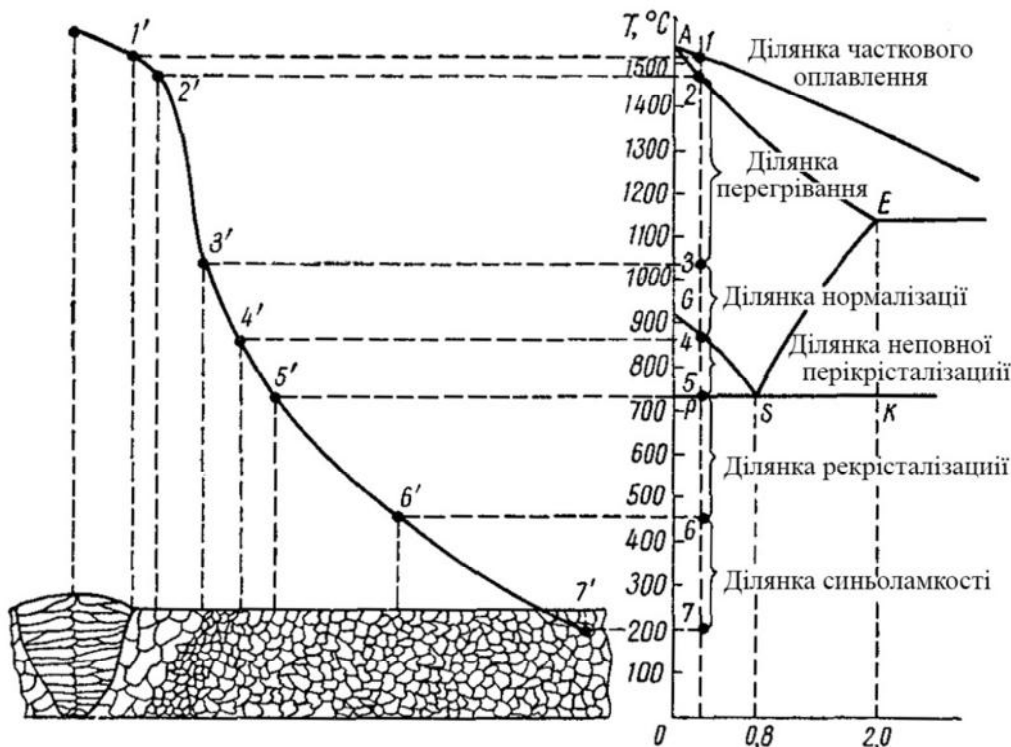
Схема будови однопрохідного зварного з'єднання вуглецевої сталі
